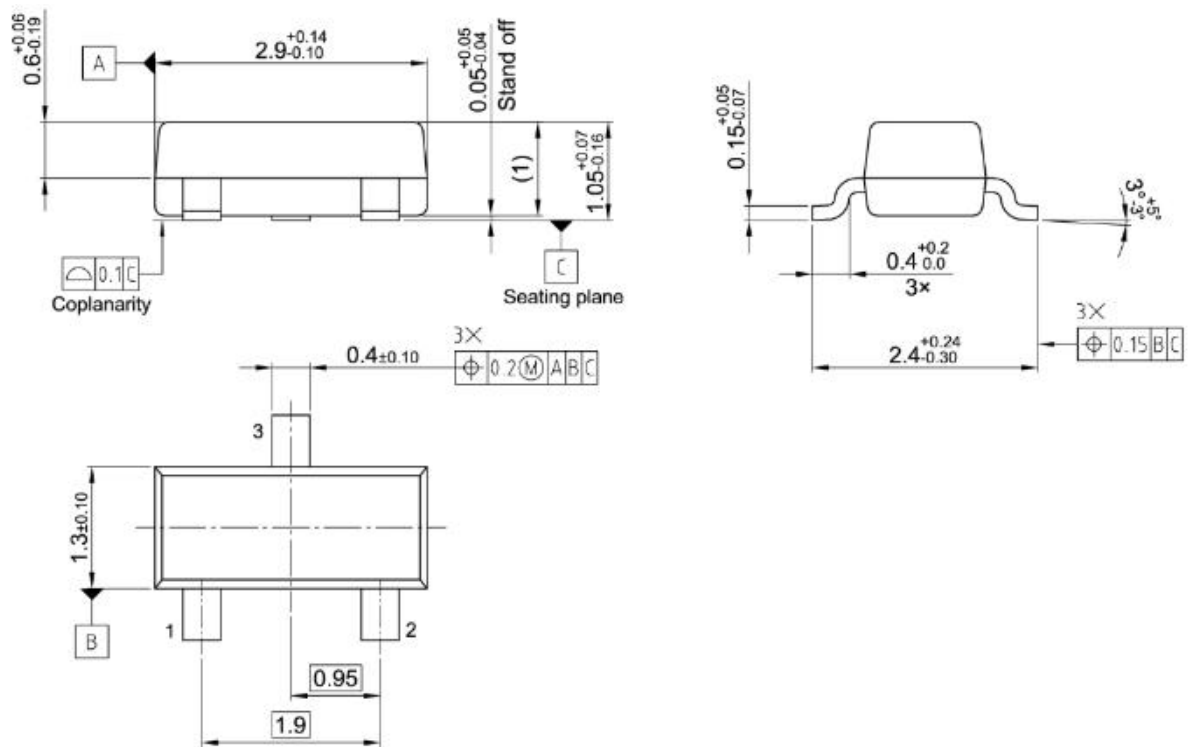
Габаритні розміри опорного регулятора напруги TL431
